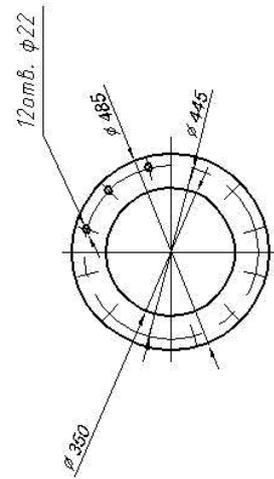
Габаритные размеры воздухо(газо)дувок типа ТВ(ТГ)-80
